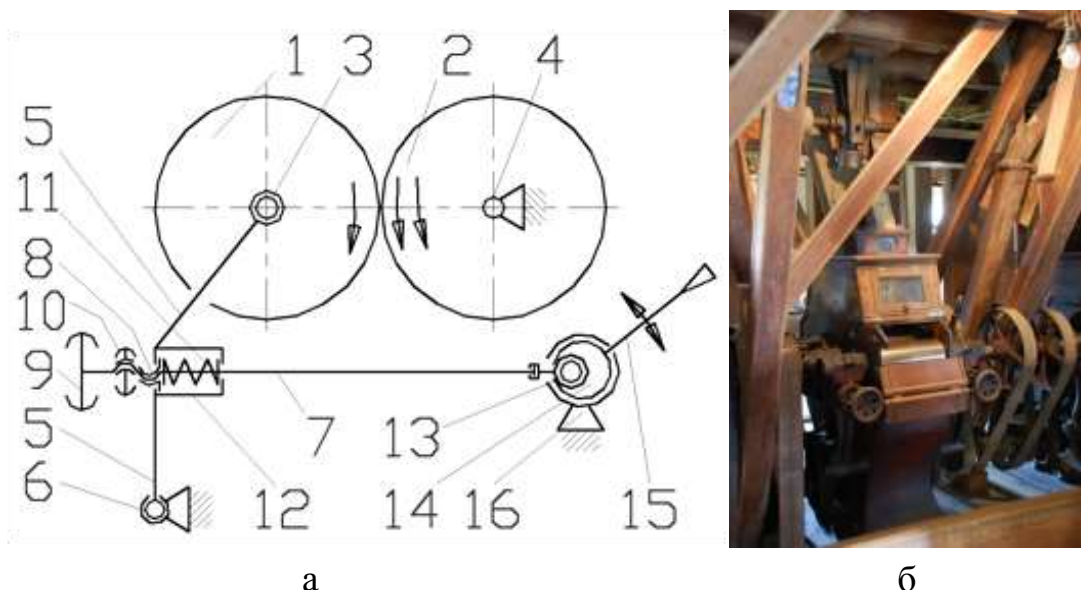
Схема а) установчого механізму і загальний вигляд б) вальцьового верстата.
